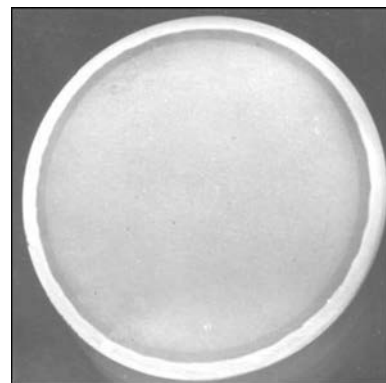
Макрошлиф поперечного сечения цилиндрической части штока задвижки DN 50, наплавленного плазменно-порошковым способом
